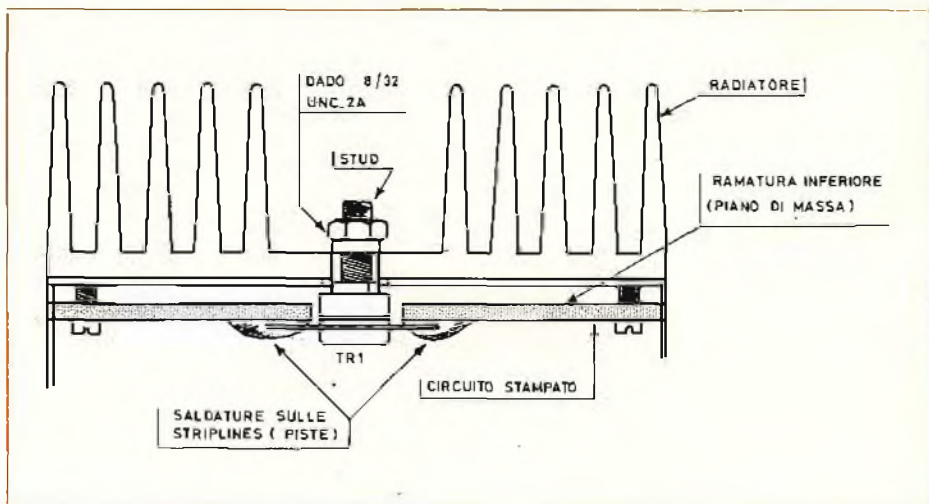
Montaggio del TR1 sul circuito stampato e dissipatore di calore.
